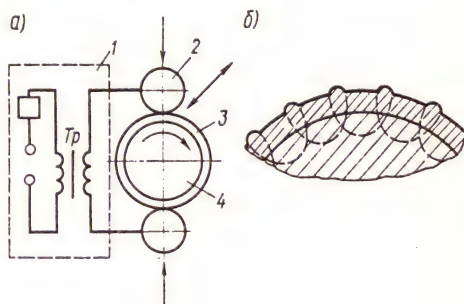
Схема наварки ленты на деталь типа вал (а) и перекрытия импульсов при наварке (б): 1 — трансформатор; 2 — электрод; 3 — лента; 4 — деталь
